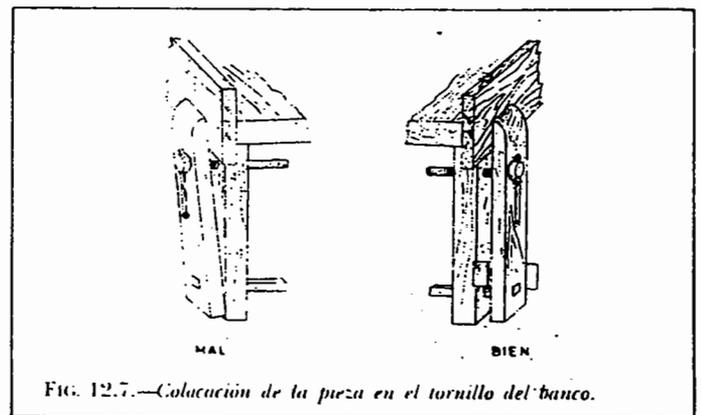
Colocación de la pieza en el tornillo del banco.
